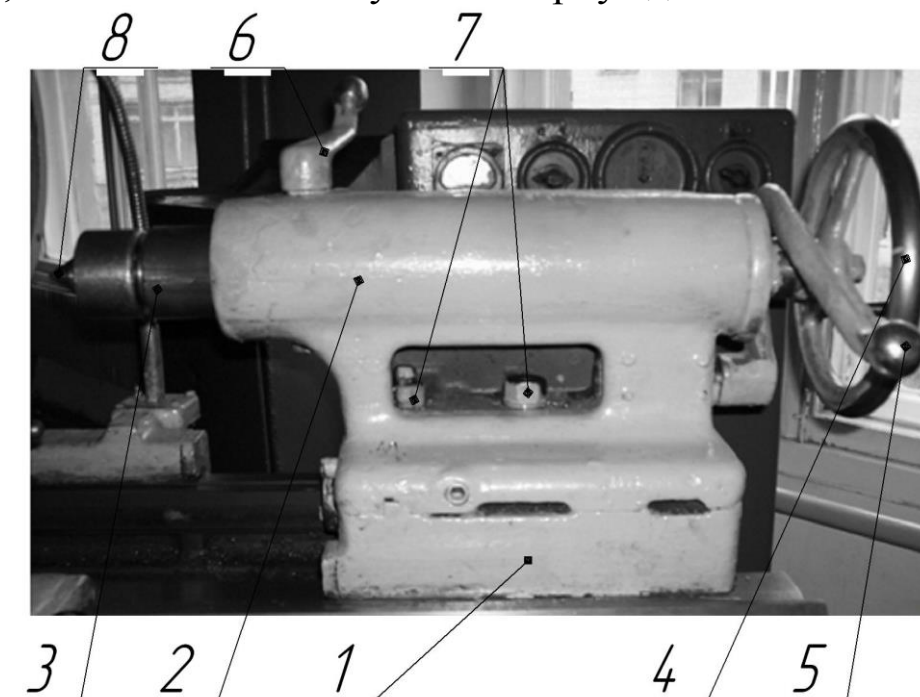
Задняя бабка: 1 – плита, 2 – корпус, 3 – пиноль, 4 – маховик, 5 – рукоятка, фиксирующая положение бабки на станине, 6 – рукоятка, фиксирующая положение пиноли, 7 – болты крепления, 8 – центр
